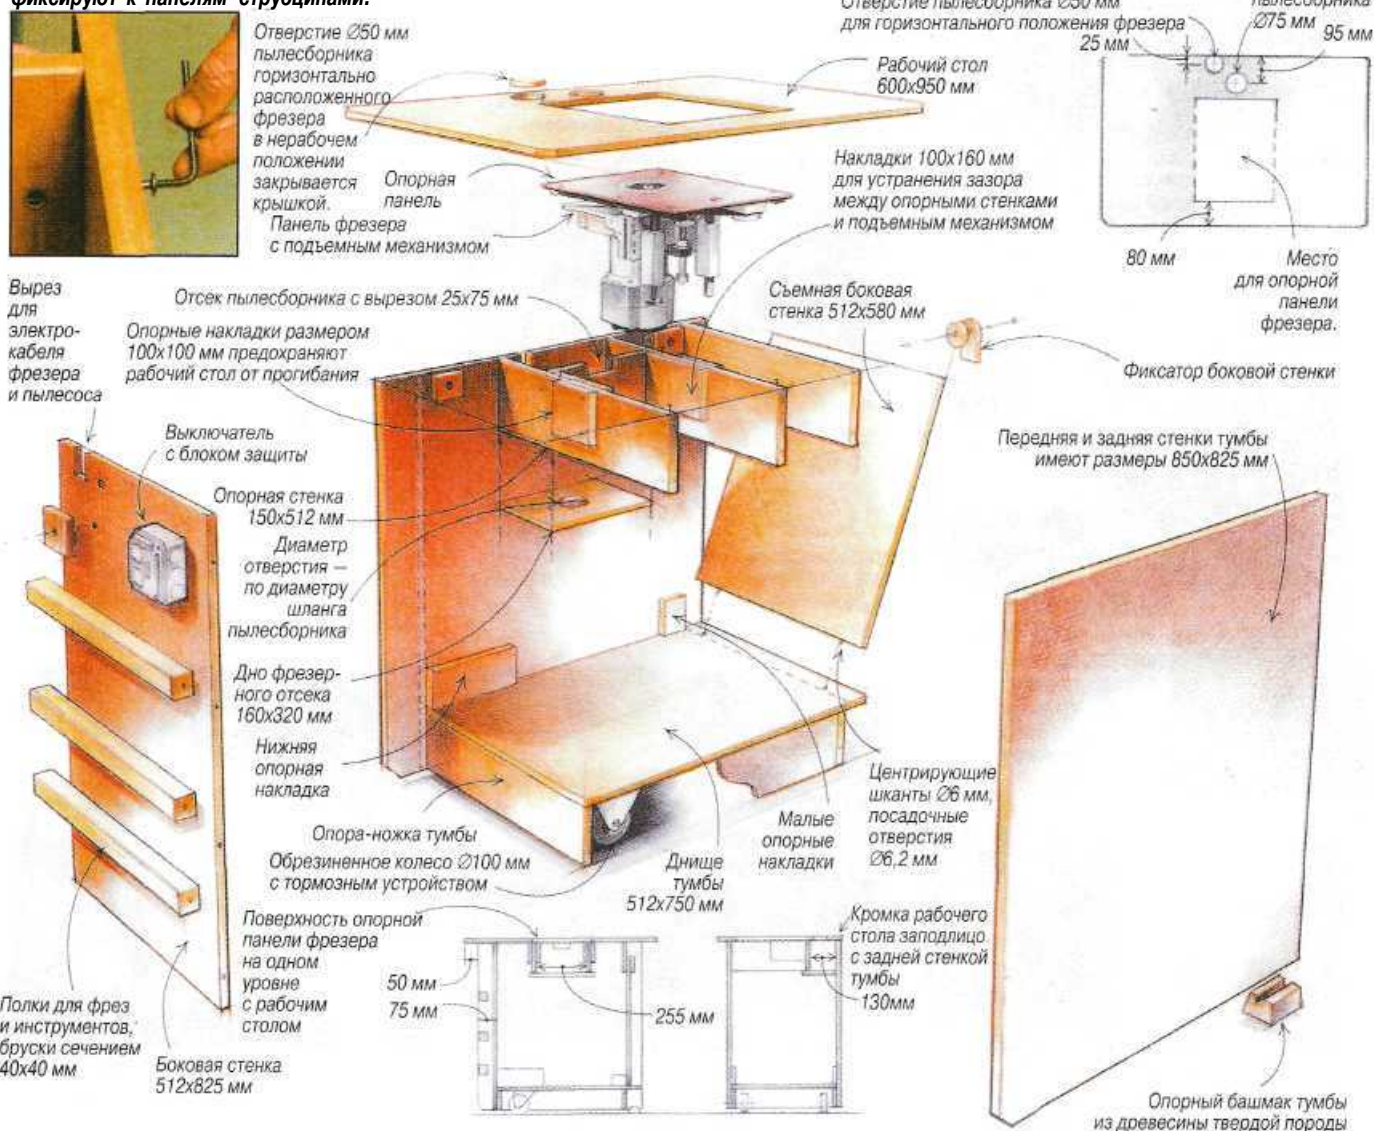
Фрезерный стол сделан из ДСП толщиной 18 мм.
